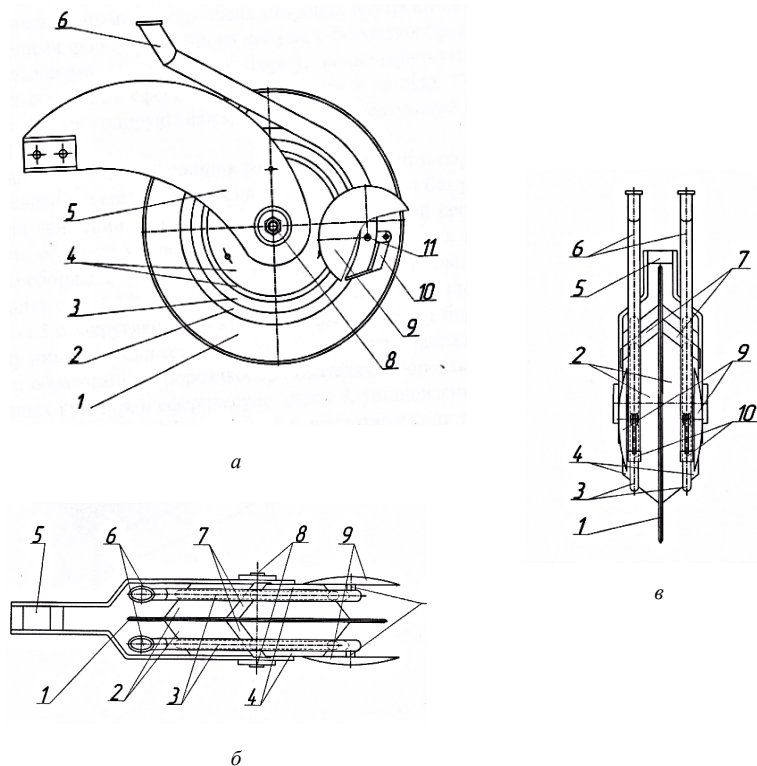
Комбинированный однодисковый сошник с двухсторонними ребрами и дисковыми загортачами с нулевым углом атаки дисков для узкорядного посева:
